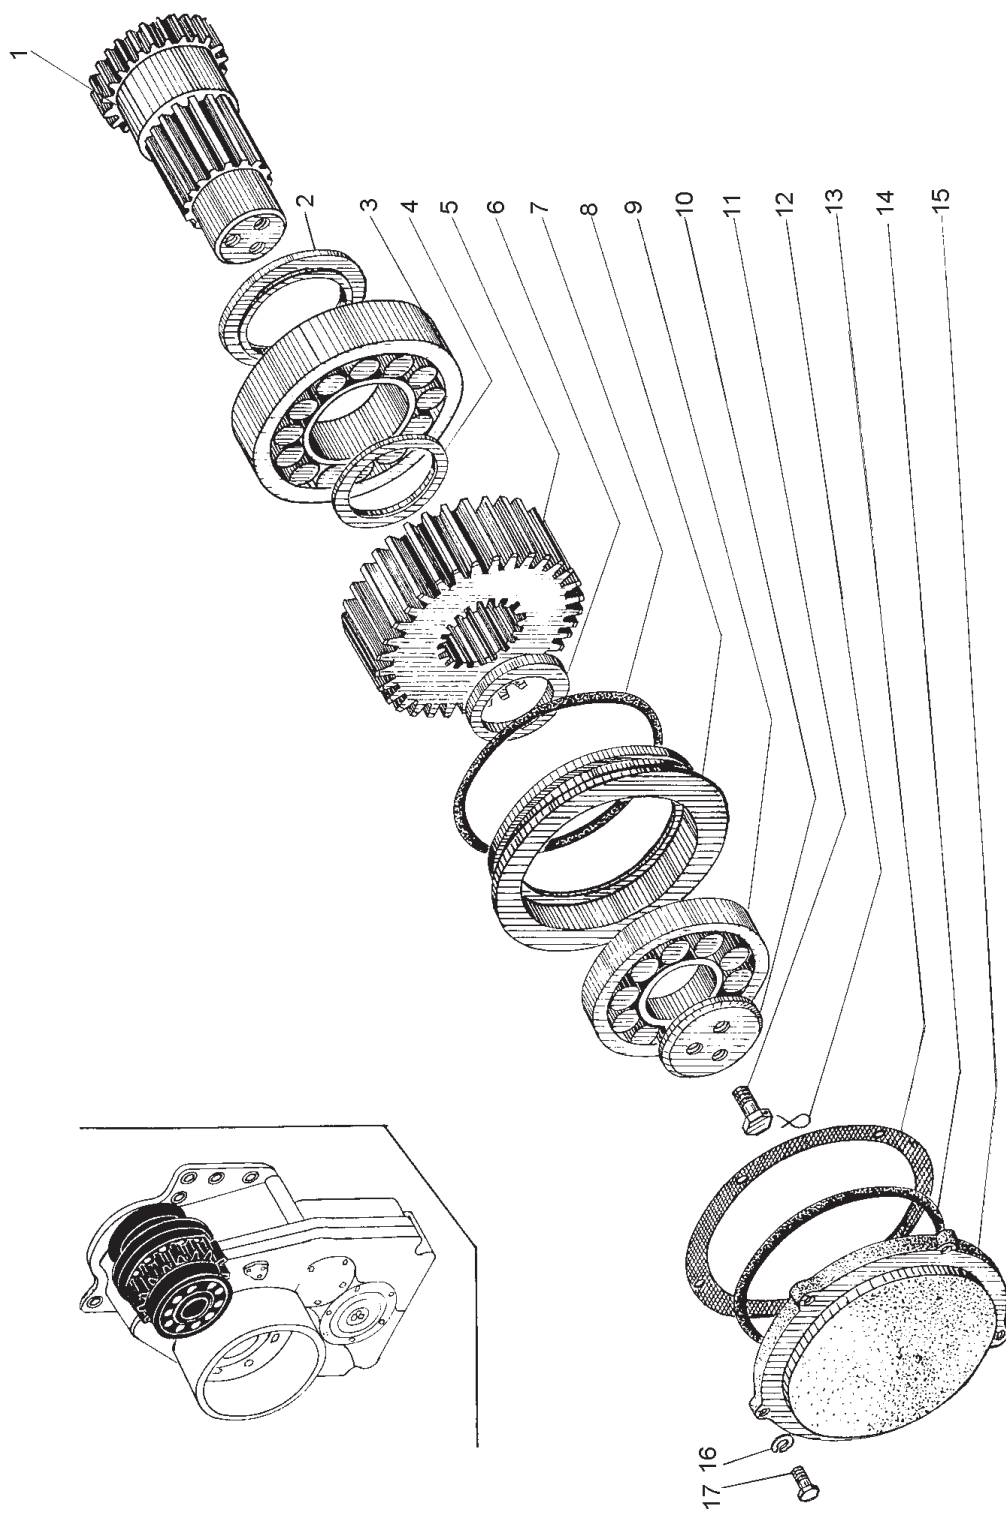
Редуктор раздаточный (ДЗ-98.10.05.000-02)
